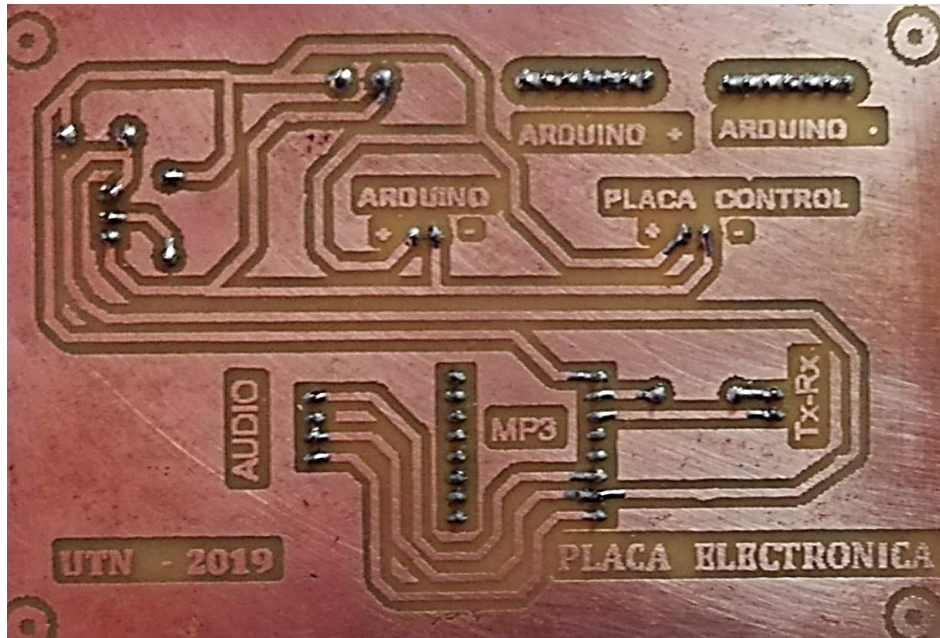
Diseño de la placa principal fundida en el ácido férrico
